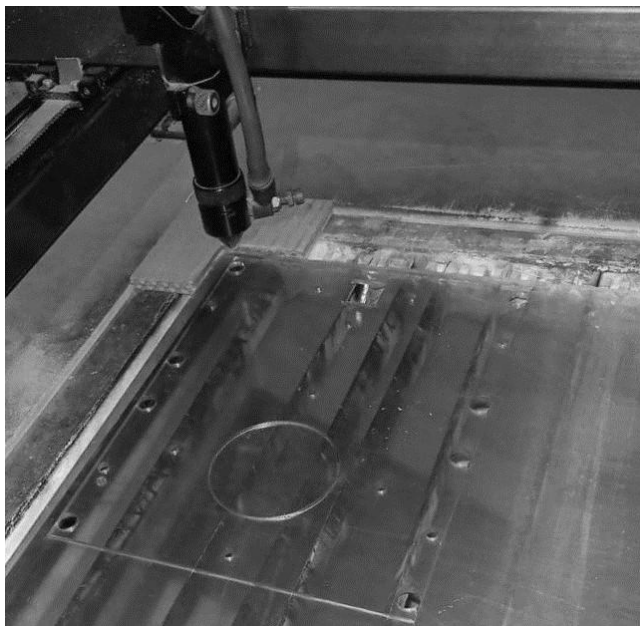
Виготовлення кришки корпусу методом лазерного різку
